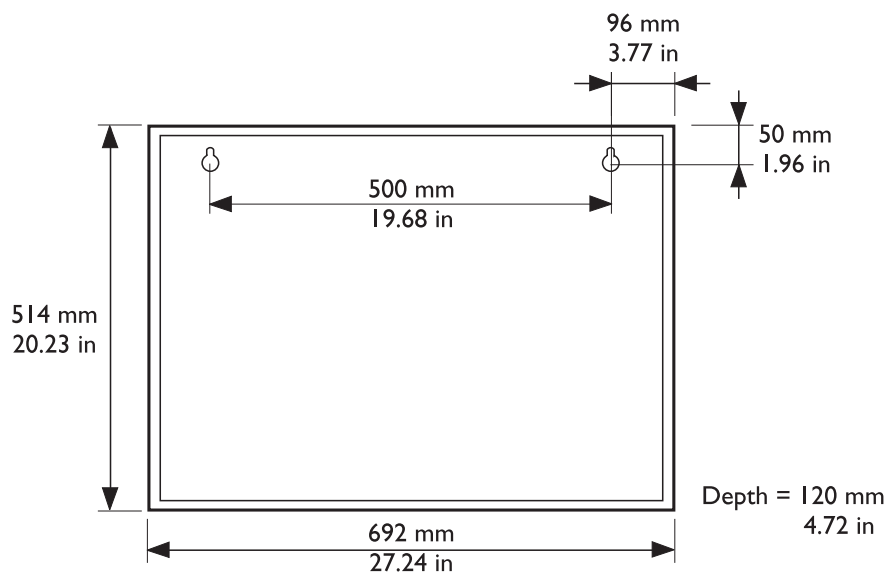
Dimensões de montagem do gabinete de carregamento
